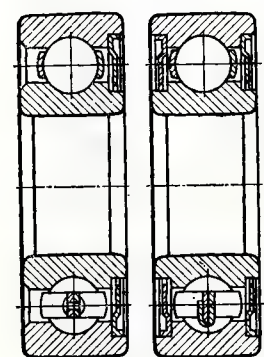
Шарикоподшипники закрытого типа с одной (а — тип 60000) и двумя защитными шайбами (б — тип 80 000)
